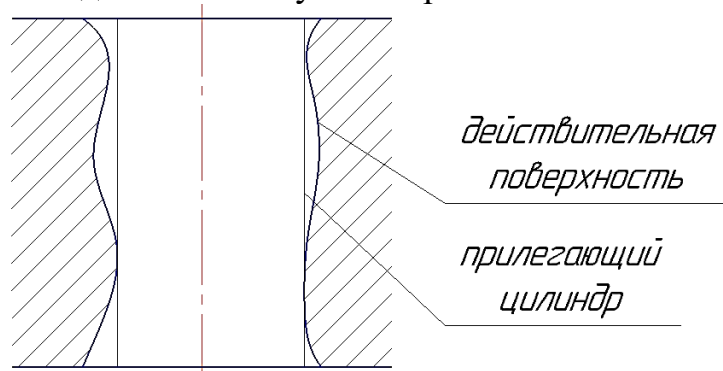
Прилегающий цилиндр для отверстия
